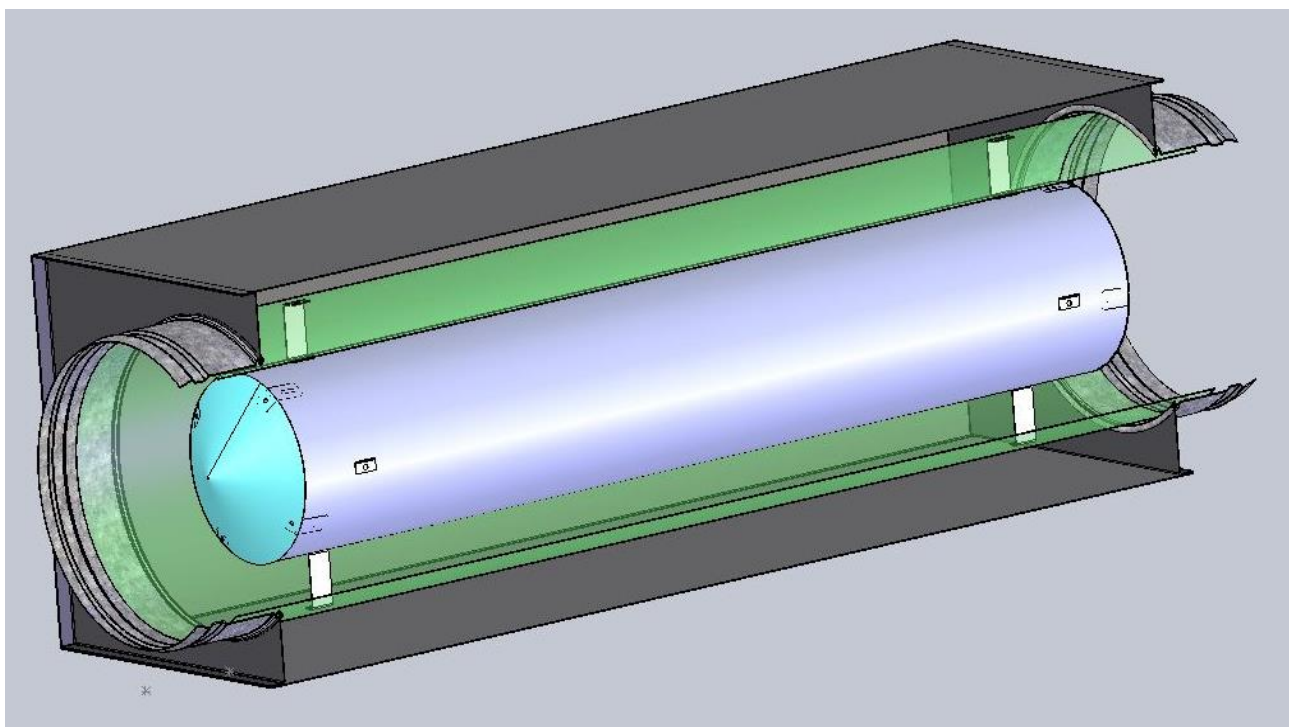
Внешний вид опытного образца канального глушителя с центральной цилиндрической звукопоглощающей вставкой.
